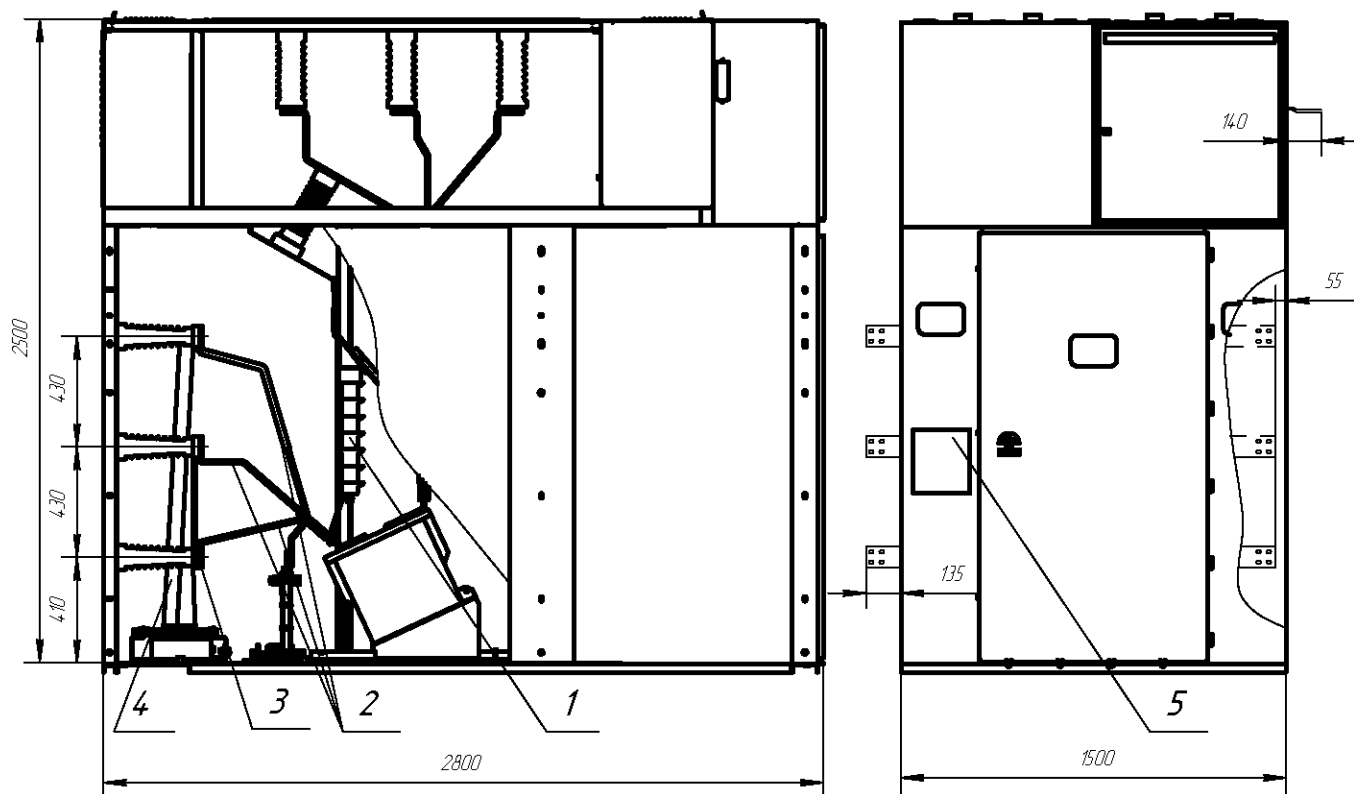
Габаритно-установочные размеры шкафа с линейными шинами для схем 05...16, 101, 102, 113, 114.
